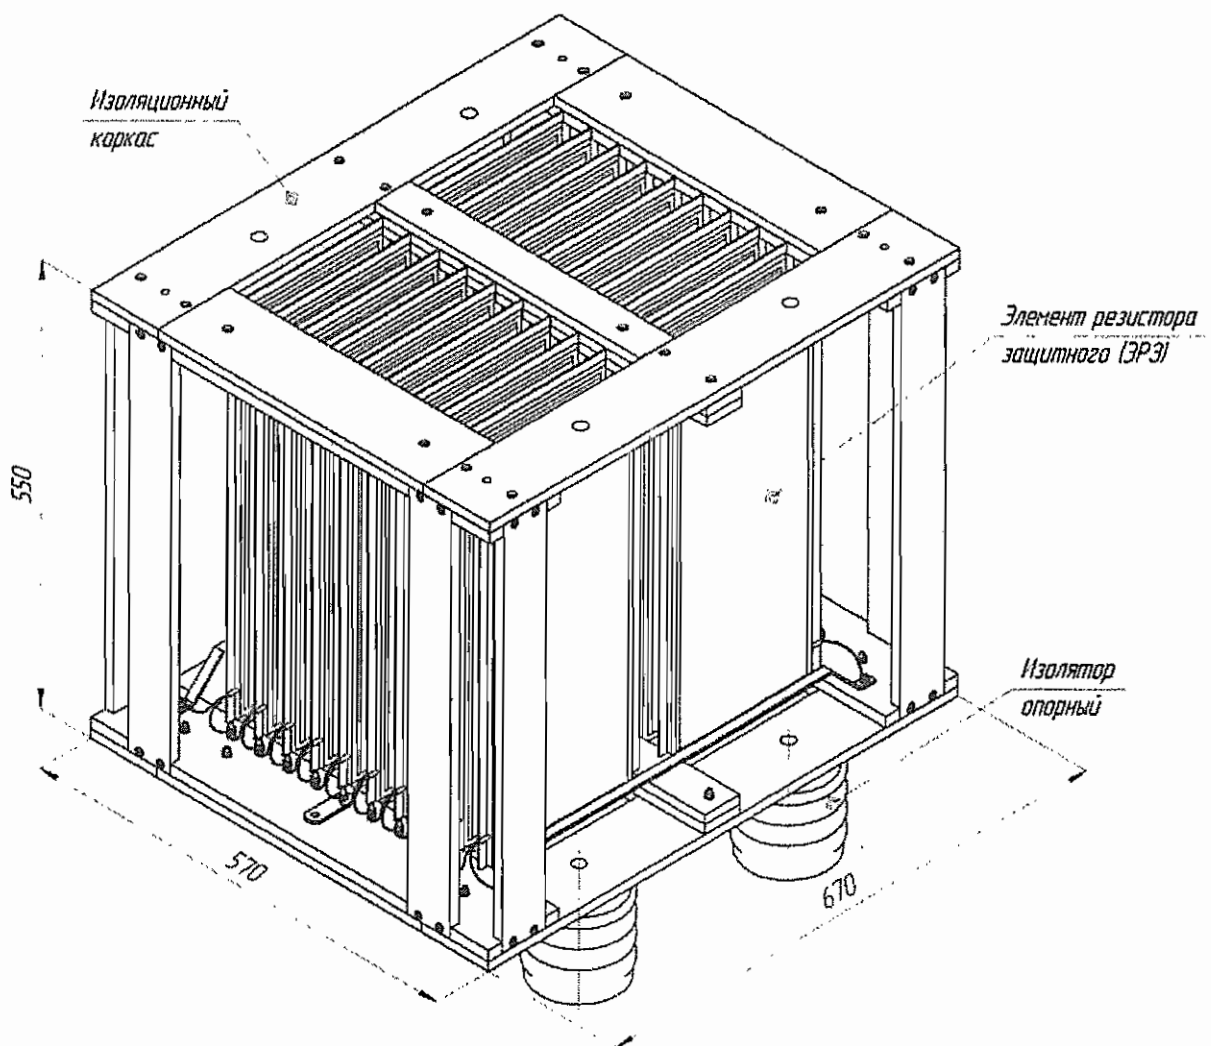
Резистор защитный типа РЗ1, тип исполнения А
